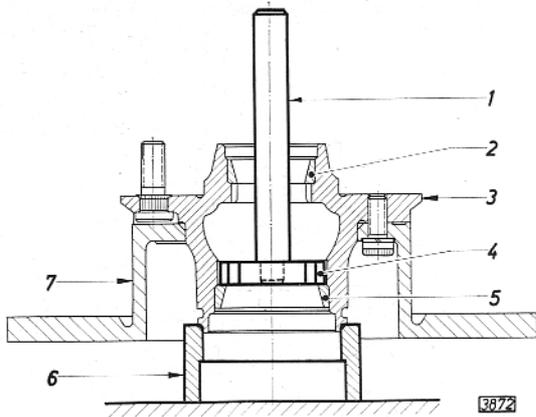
Äußeren Laufring des inneren Radlagers herauspressen
